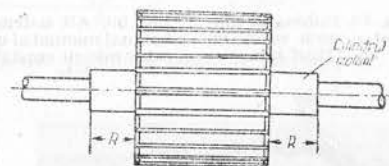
Izolarea axului la rotorii mici prin cilindri izolanti.
